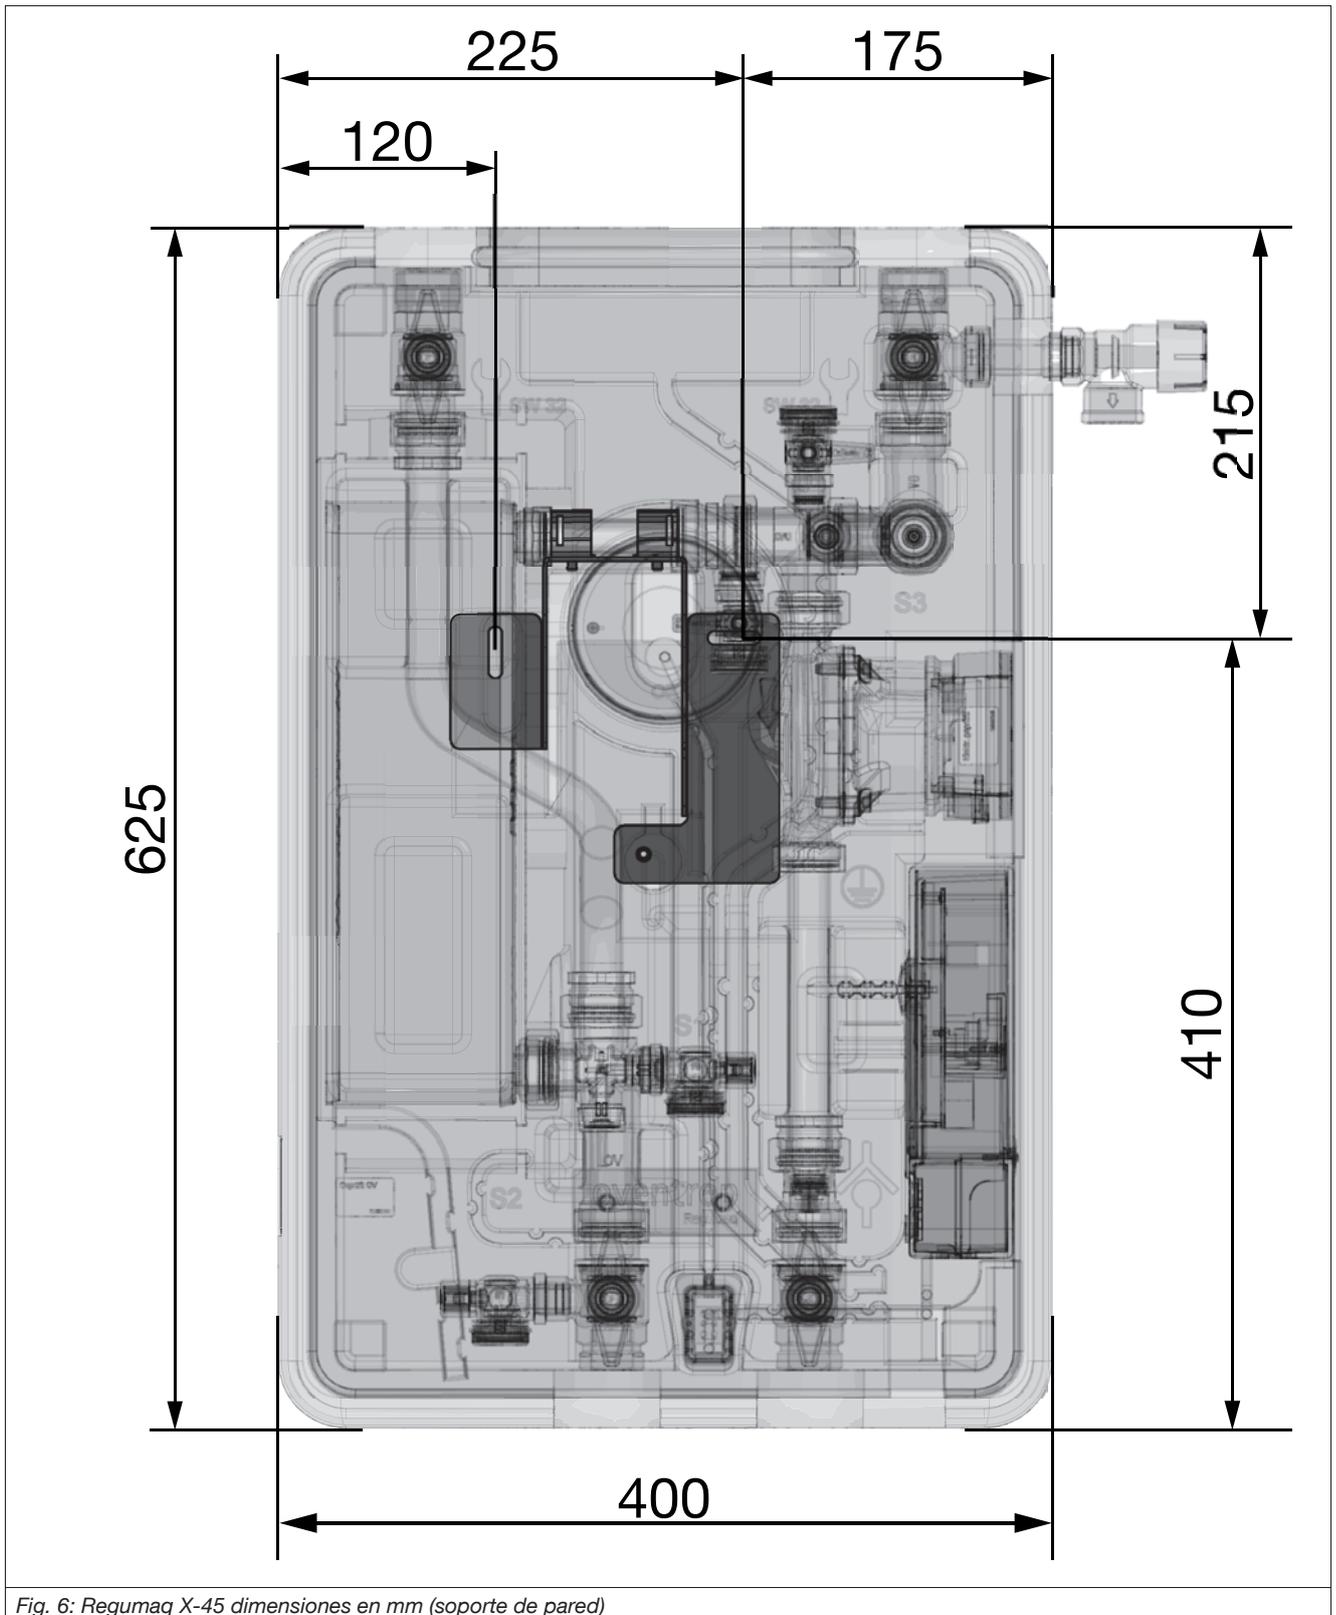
Regumaq X-45 dimensiones en mm (soporte de pared)
